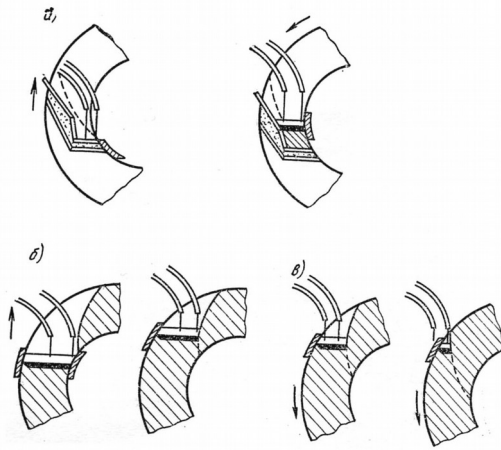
Схема проведения сварки кольцевого шва
